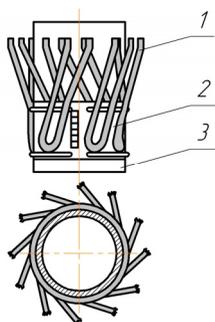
Скребок разъемный типа СК: 1 – рабочий элемент; 2 – корпус; 3 – штырь
